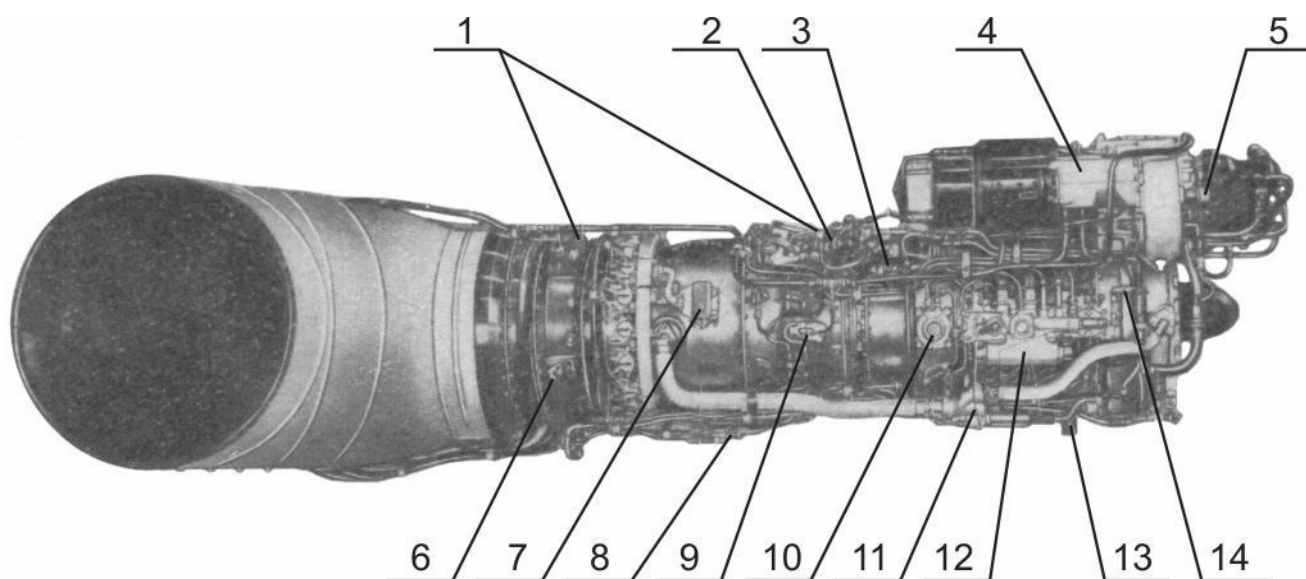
Двигатель ТВ2-117А (вид справа):
